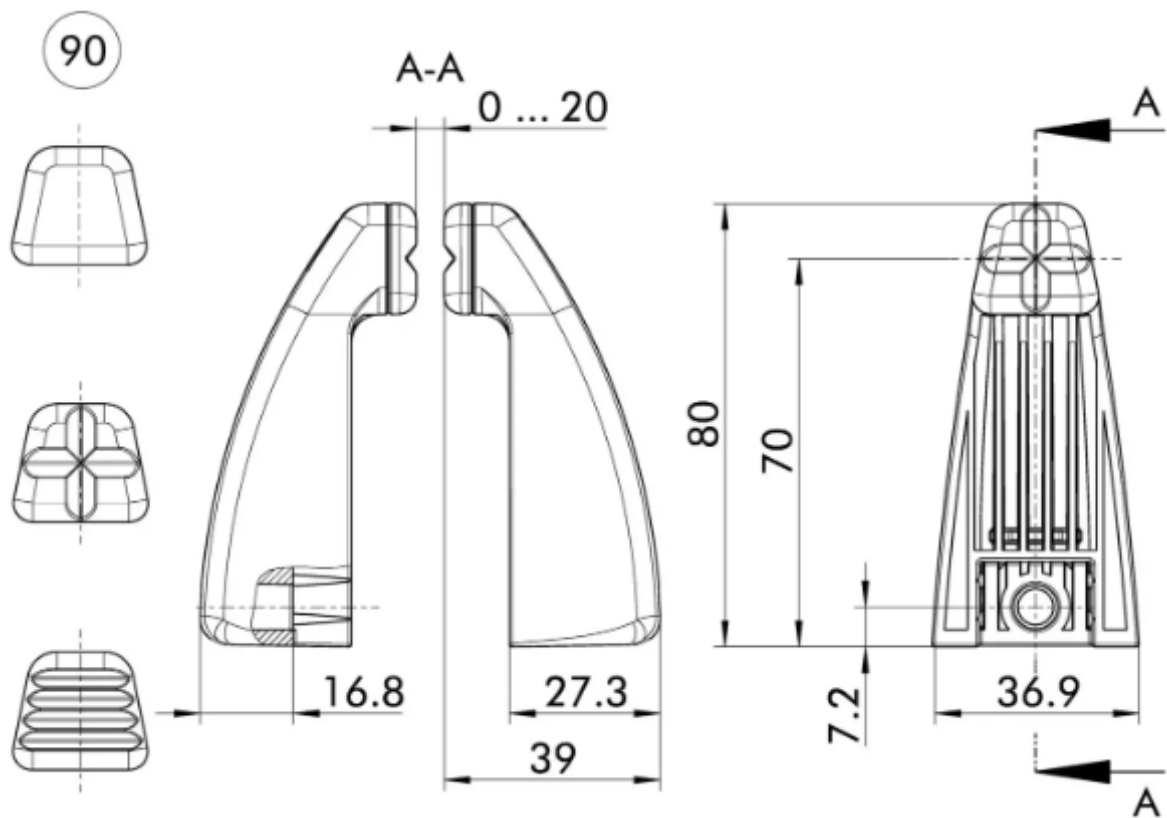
Plano pinza oficial GoFa CRB 15000
